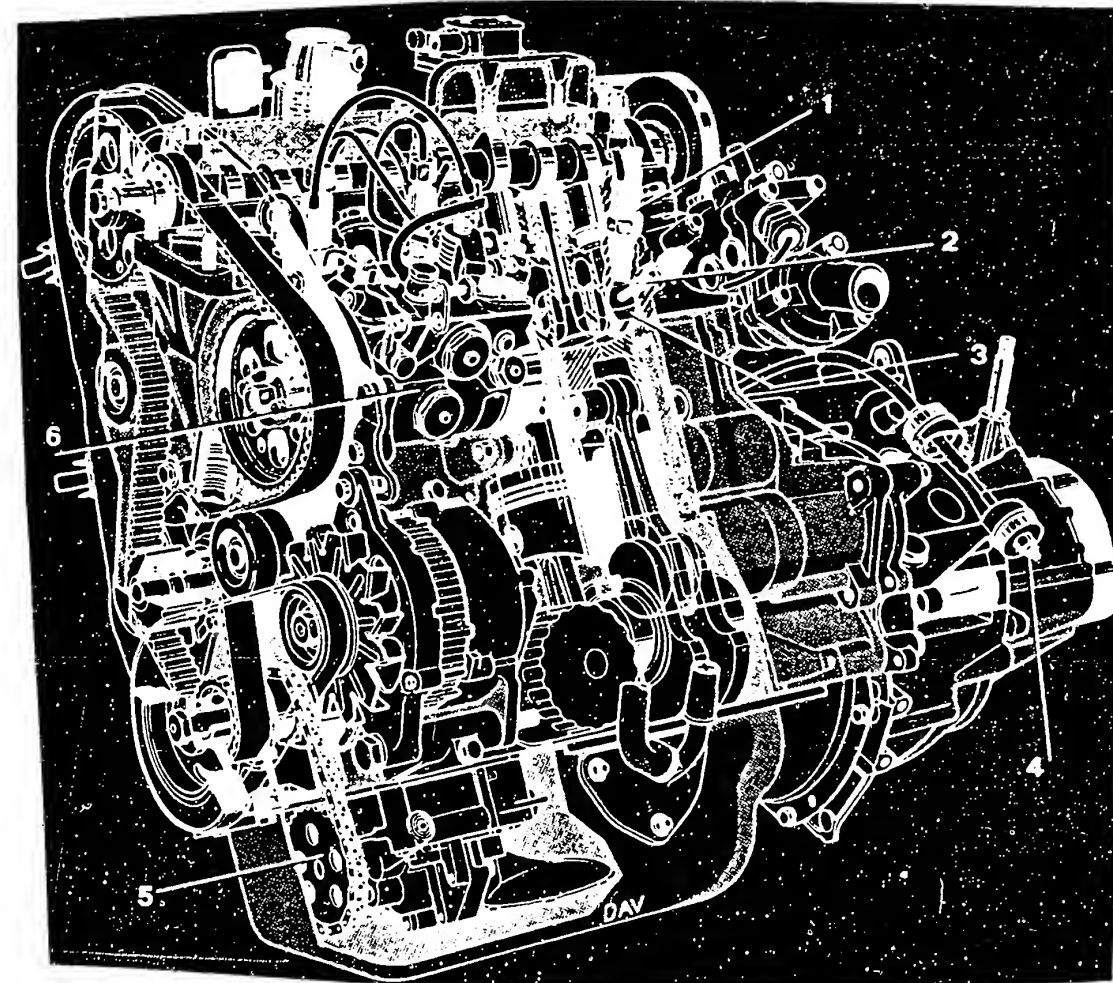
Der X4D7 Dieselmotor teilweise geschnitten. Es bedeuten: 1 Einspritzdüse – 2 Glühstift – 3 Wirbelkammer – 4 Kupplungsseilzug mit Ausrückgabel – 5 durch Kette angetriebene Ölpumpe – 6 Roto-Diesel-Verteilereinspritzpumpe.
